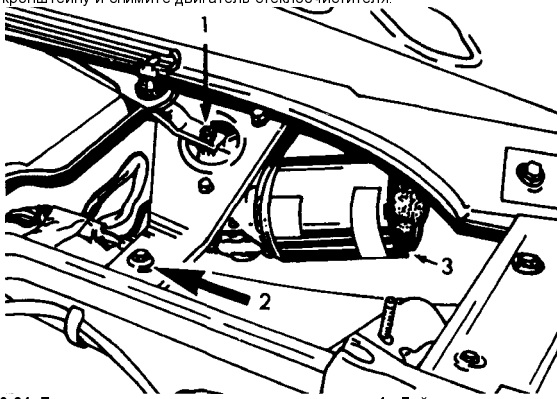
Двигатель и механизм стеклоочистителя. 1 - Гайка крепления рабочего рычага. 2 - Болт крепления кронштейна двигателя стеклоочистителя. 3 - Двигатель стеклоочистителя.
